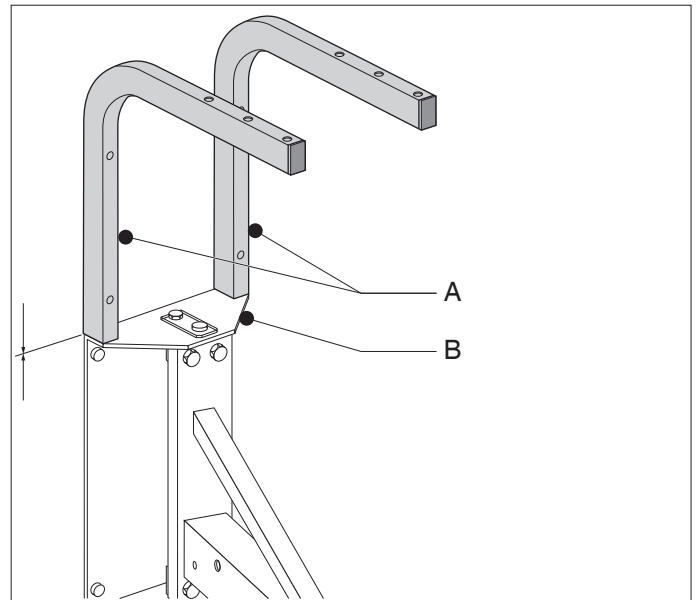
Montaggio delle staffe di montaggio TNB (opzione)
